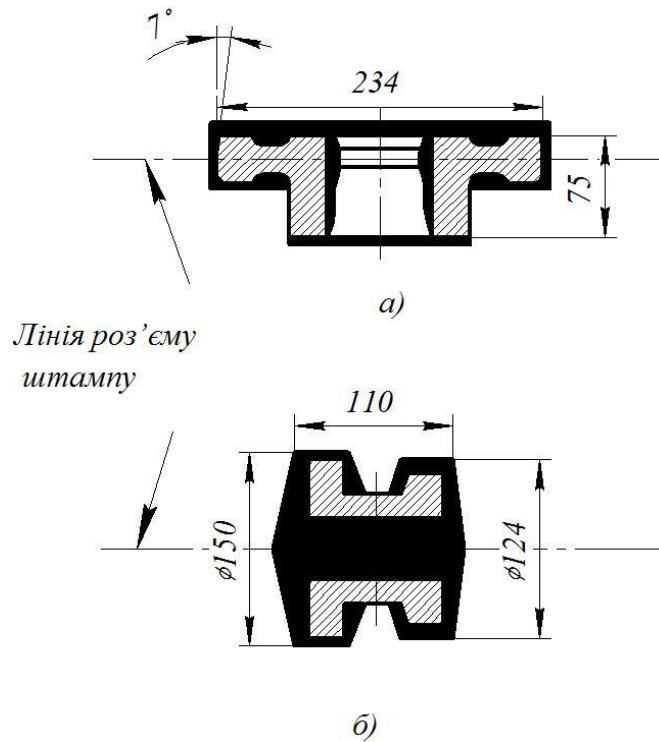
Штамповані заготовки для зубчастих коліс:
